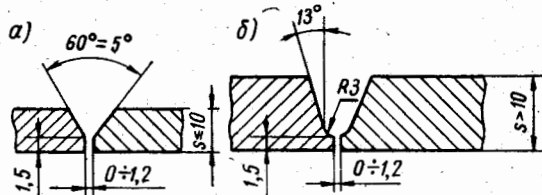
Конструктивные элементы подготовки кромок листовой латуни марки Л62, свариваемой встык электродуговой сваркой угольным электродом (по ОН 26-01-71-68): а — V-образная разделка кромок; б — V-образная разделка кромок с криволинейным скосом
